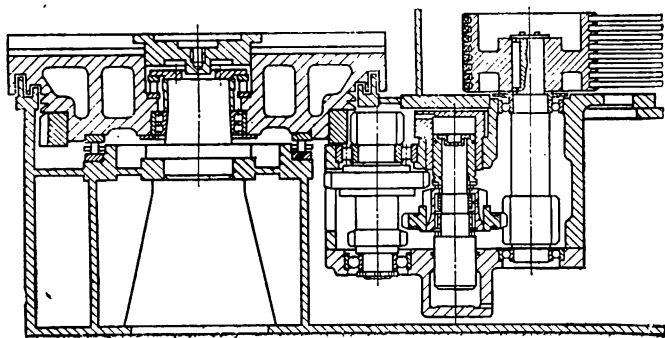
Схема стола на подшипниках качения с центрированием планшайбы подшипником с коническим внутренним отверстием и коробкой скоростей с вертикальным расположением валов
